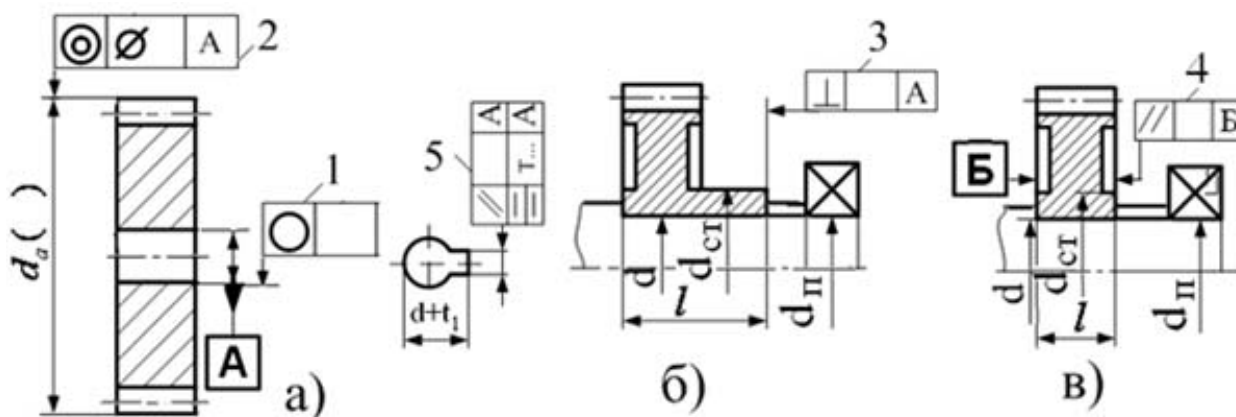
Допуски циліндричності посадочних поверхонь шестерні
